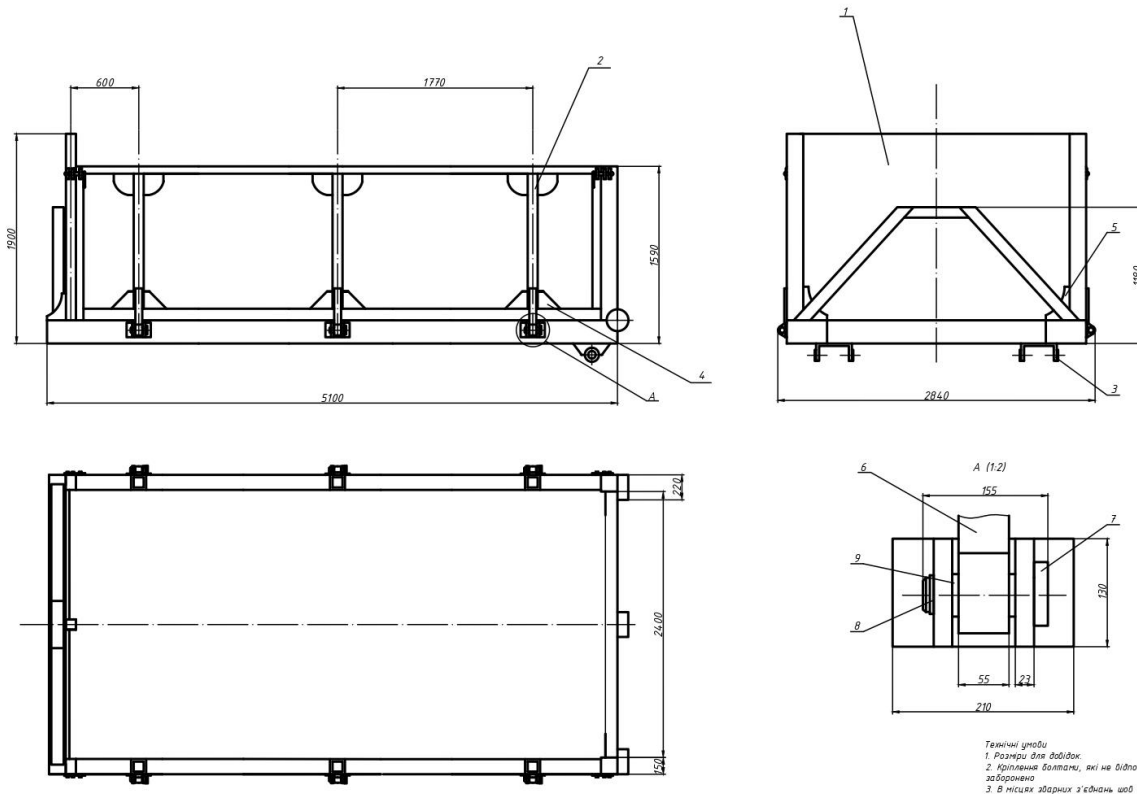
Конструкція саморозвантажувального бортового кузова машини для транспортування дров:
